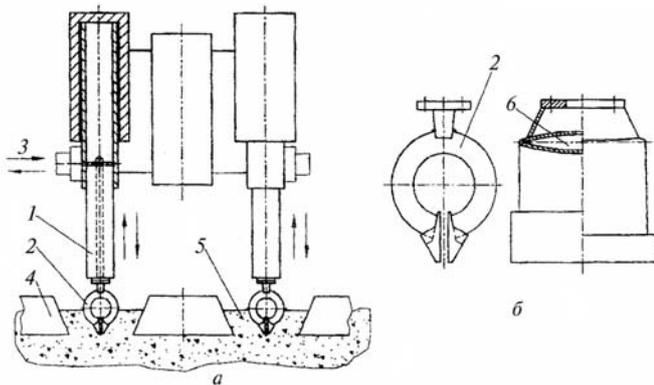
Конструктивная схема шпалоподбивочного блока с рабочими органами в виде трубчатых пружин (а) и поперечное сечение трубчатой пружины (б):
